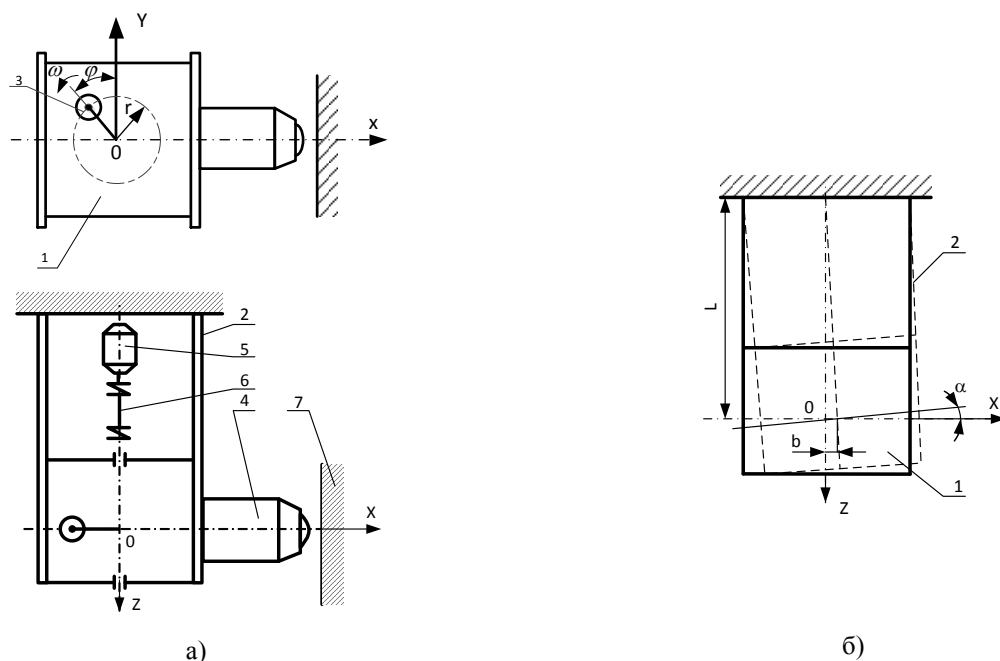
Схема эксцентрикового упрочнителя (а) и повороты корпуса упрочнителя в процессе колебаний (б): 1 – корпус; 2 – плоская пружина; 3 – эксцентриковая масса; 4 – инструментальная головка; 5 – электродвигатель; 6 – гибкий вал; 7 – ограничитель (обрабатываемая деталь)
